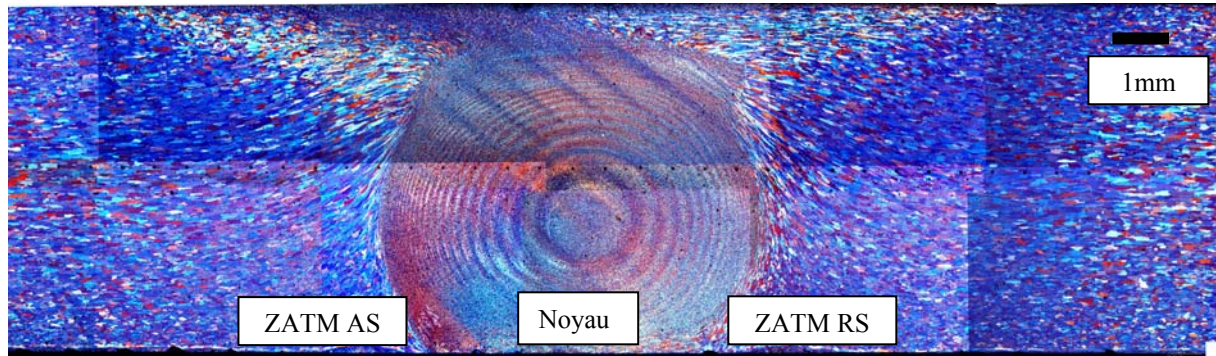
Cartographie d'un joint soudé 2024 T351 après attaque anodique. Microscopie optique
